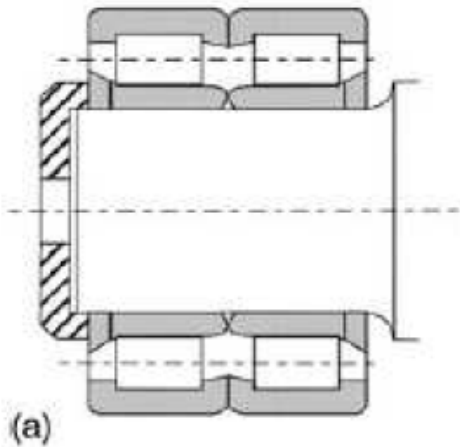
Rodamiento de Rodillos Cilíndricos.
